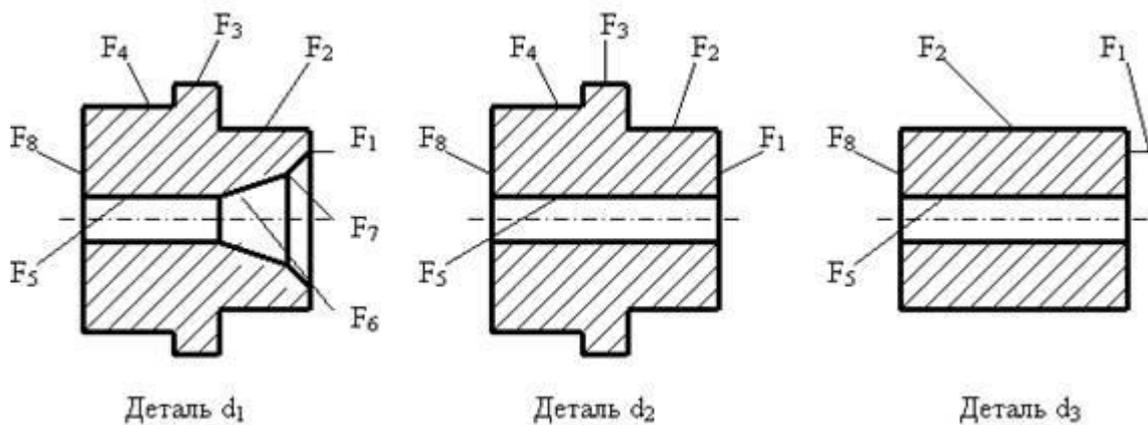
Ескіз деталей для обробки на прутковому токарському автоматі
